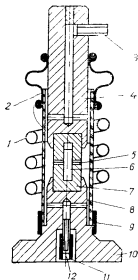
Оснастка для сварки датчика токами высокой частоты
